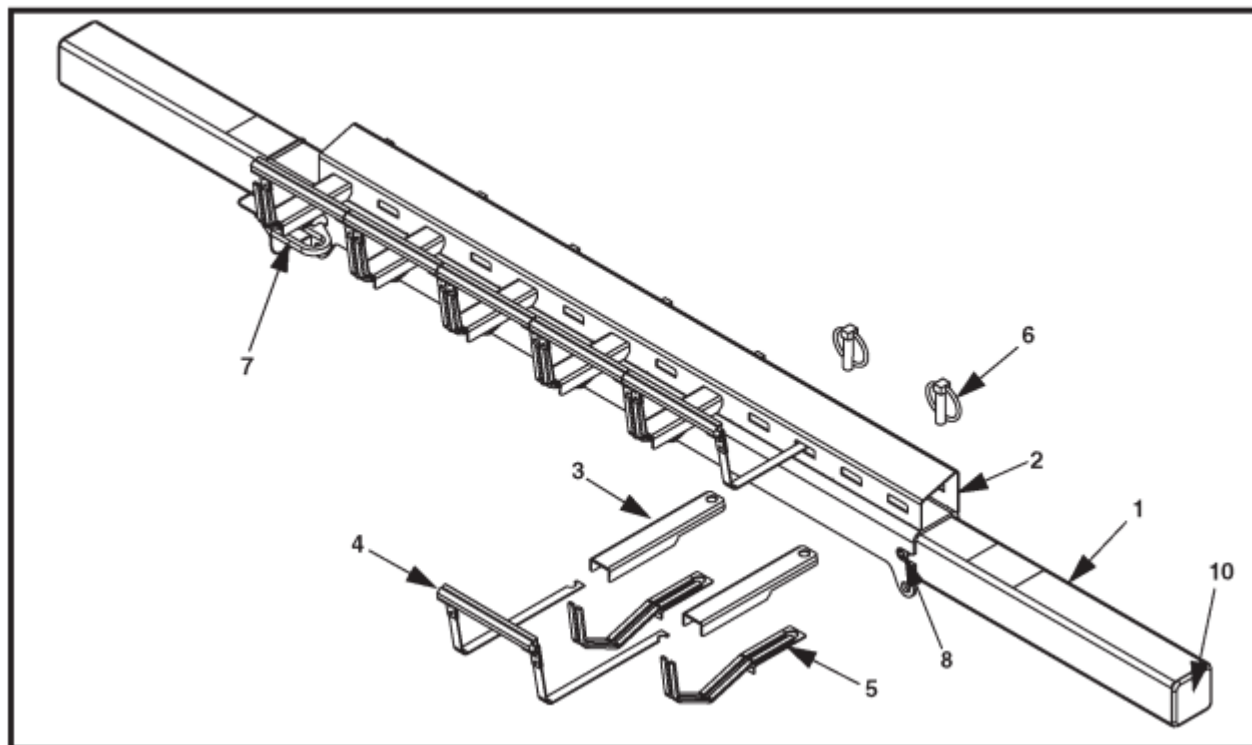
Вторичный скребок Cleanscrape®, Н/Д C2C1SXXXXXXXXX
